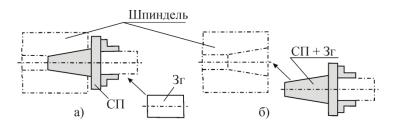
Схемы СП нашпиндельного типа: стационарного (а) и приспособления-спутника (б)
